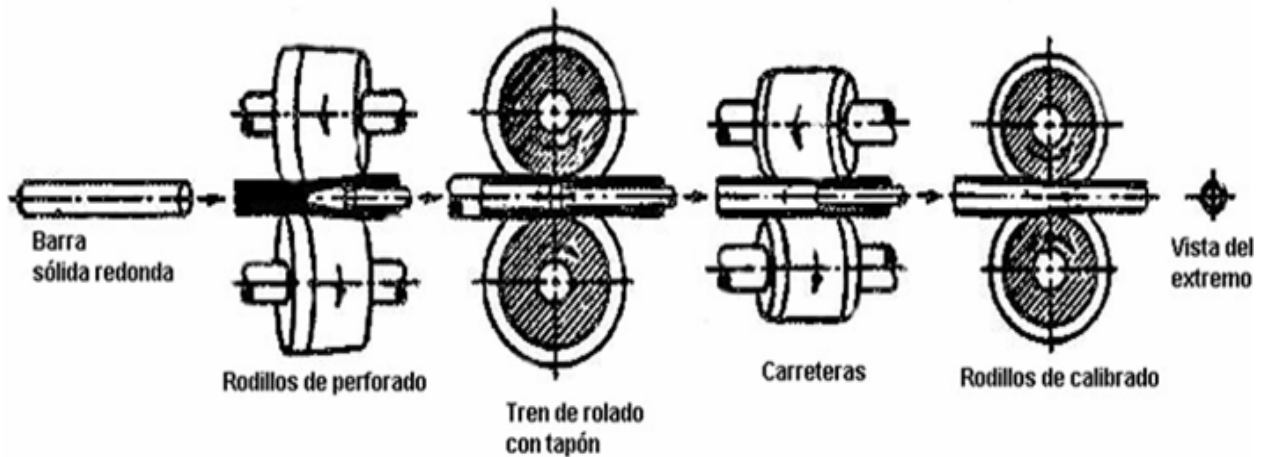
Principales Pasos en la manufactura de Tubería sin Costura
